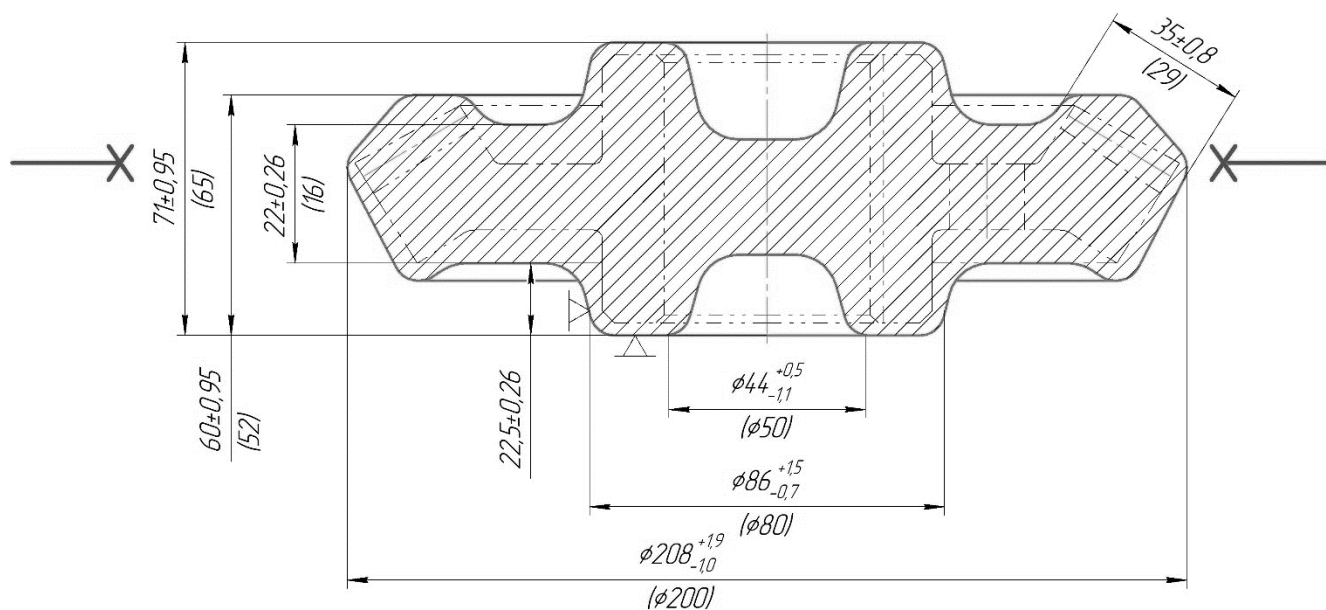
Ескіз заготовки, яка отримана штамповкою на КГШП
